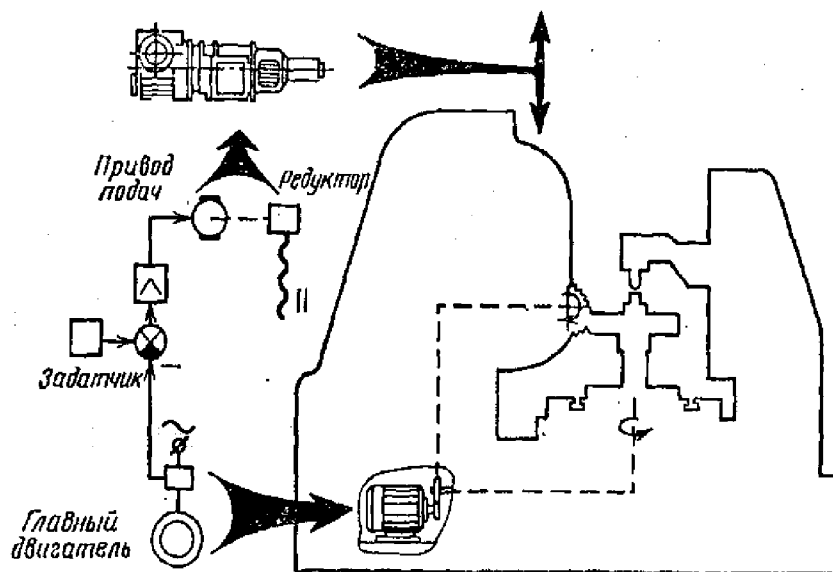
Схема адаптивної системи привода зубообробного верстата 5К324
